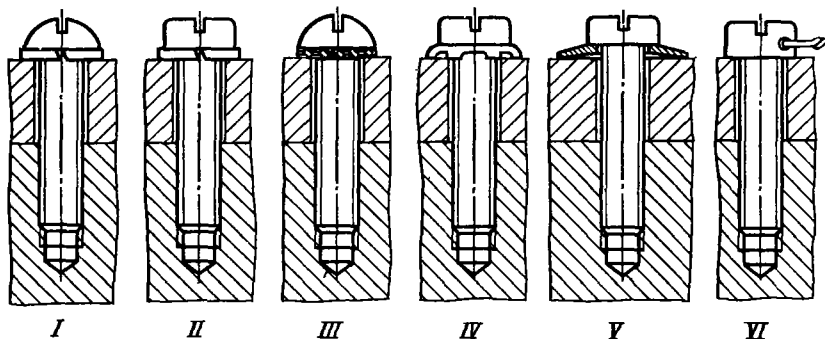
Стопорение винтов с полусферической и цилиндрической головками:
